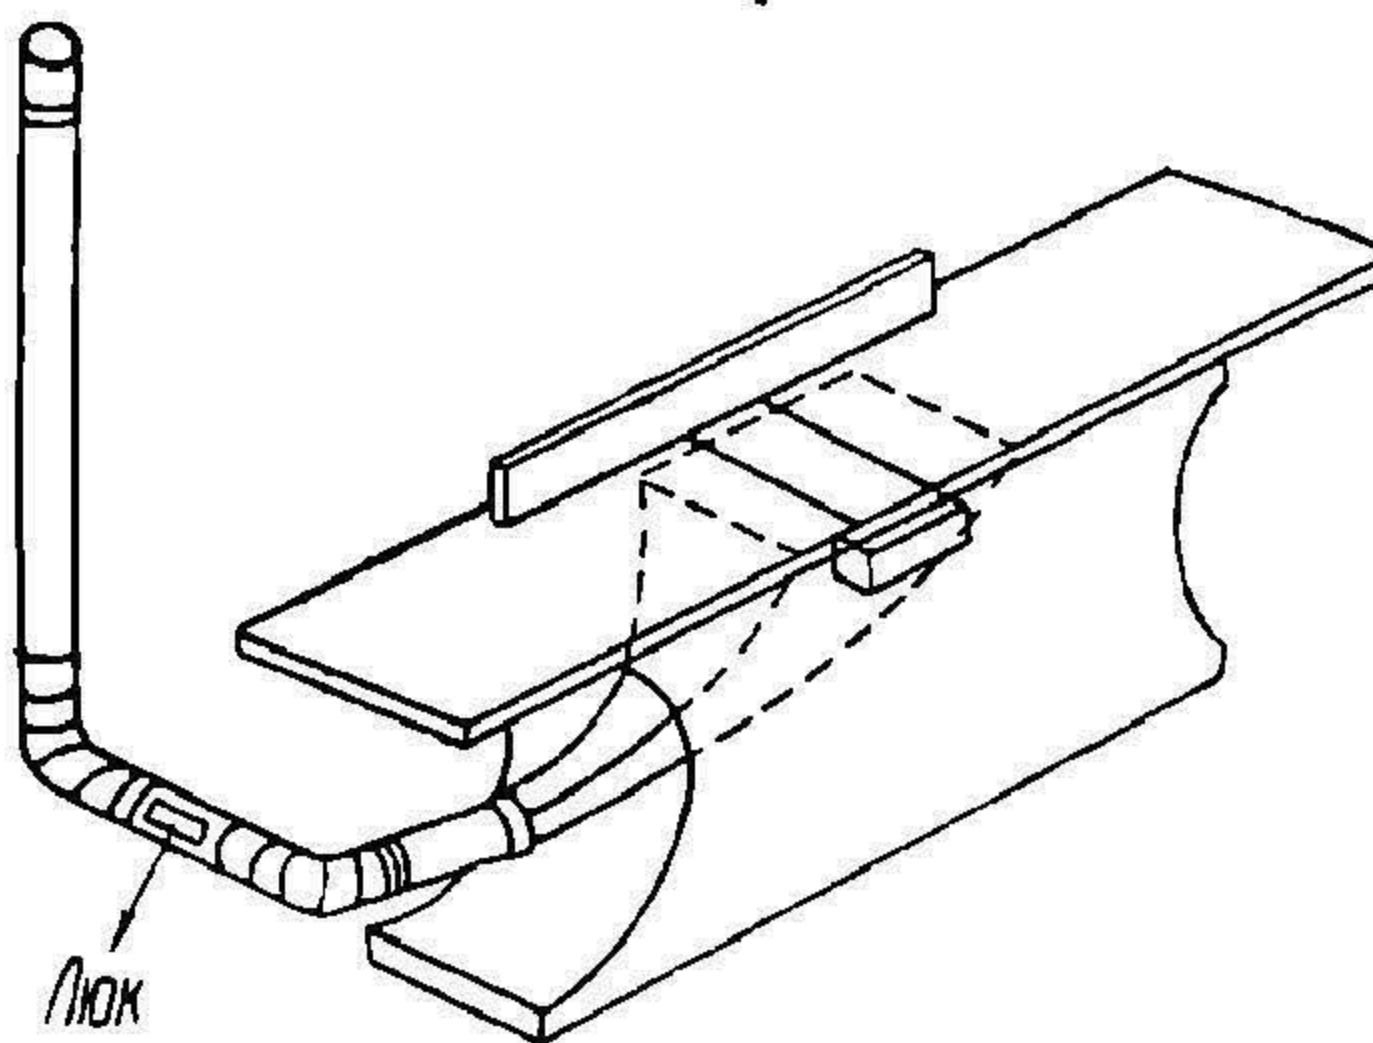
Вытяжка опилок из-под ножей фуговочного станка.
